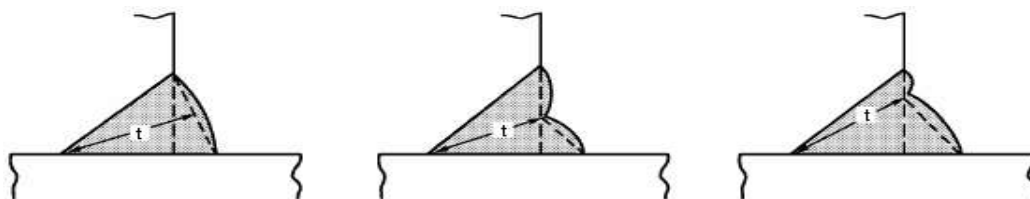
Tamaño de la garganta efectiva soldadura tipo filete
